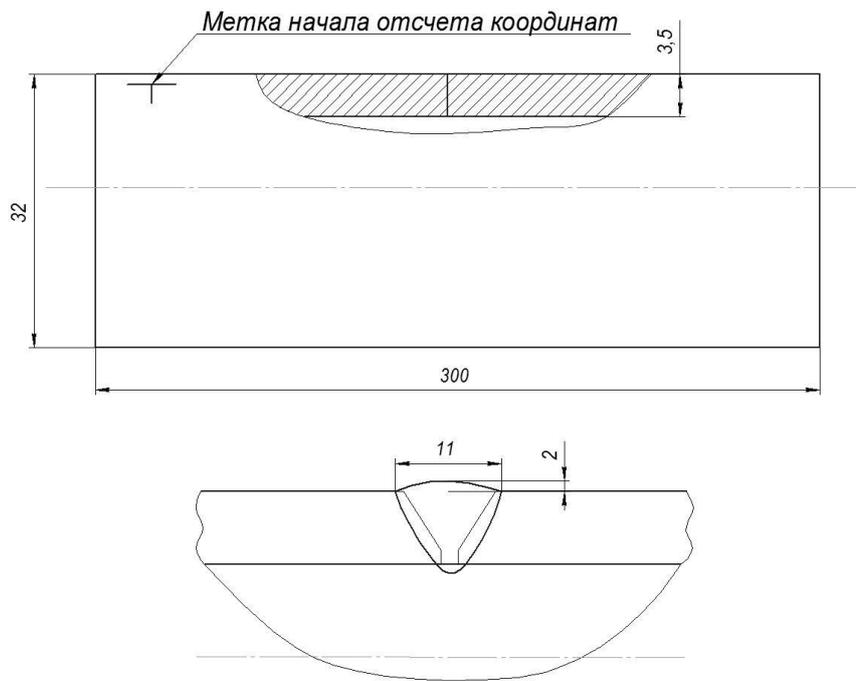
Эскиз сварного соединения и образца
